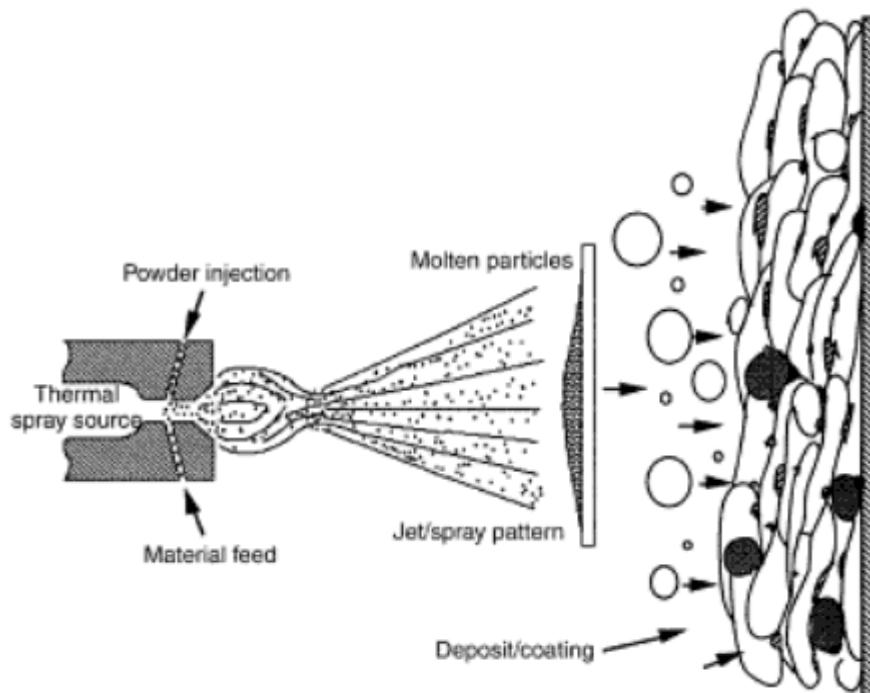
Типовий процес термічного напилення та формування покриття
